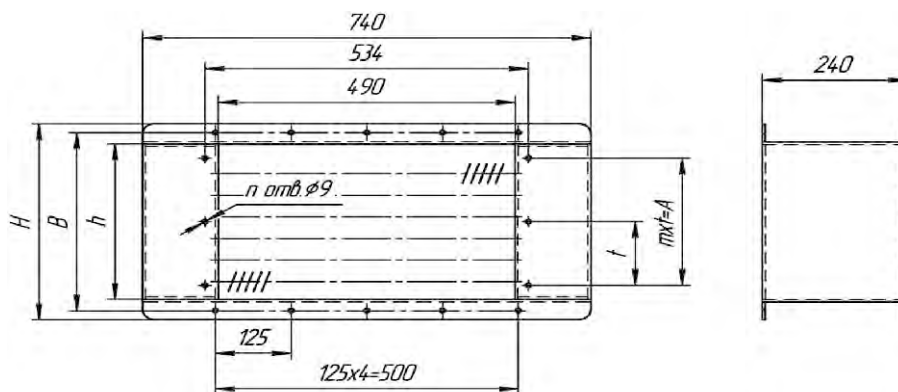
Габаритные и присоединительные размеры воздухонагревателей электрических ВНЭ.
